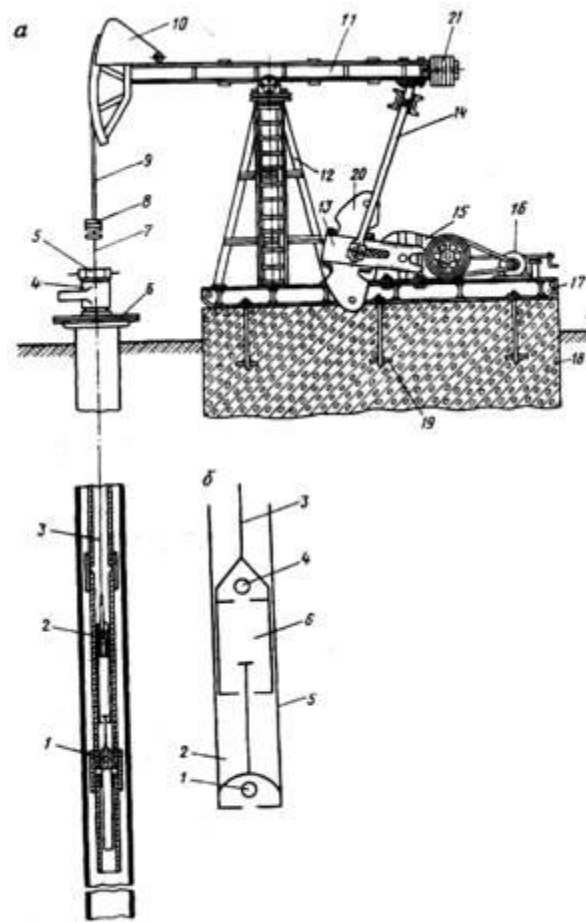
Схема штангової насосної установки: а – загальна схема: 1 – свердловинний насос; 2 –насосно-компресорні труби; 3 – штанги; 4 – трійник; 5 – сальник; 6 – план-шайба; 7 – полірований шток; 8 – траверси; 9 – підвіска; 10 – головка балансира; 11 – балансир; 12 – опора; 13 – кривошип; 14 – шатун; 15 – редуктор; 16 – електродвигун; 17 – рама; 18 – бетонна основа; 19 –анкерні болти; 20 – роторна противага; 21 – балансирна противага
